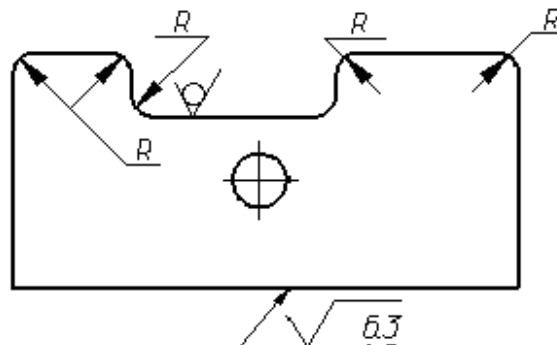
Пример обозначения шероховатости поверхности, плавно переходящей одна в другую.
